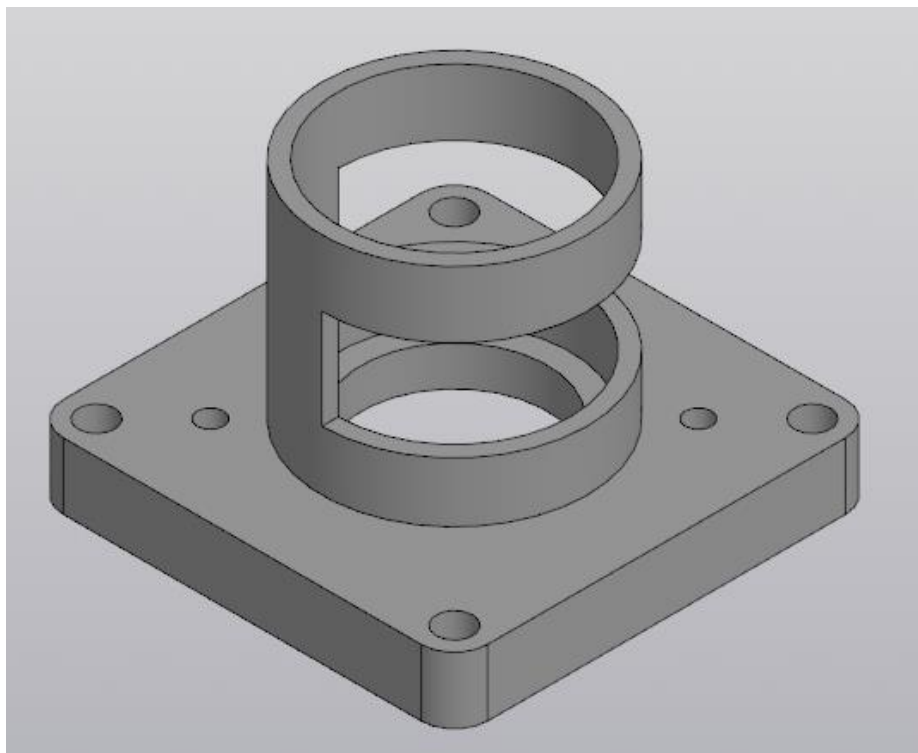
Твердотельная модель детали «Корпус подшипника»
